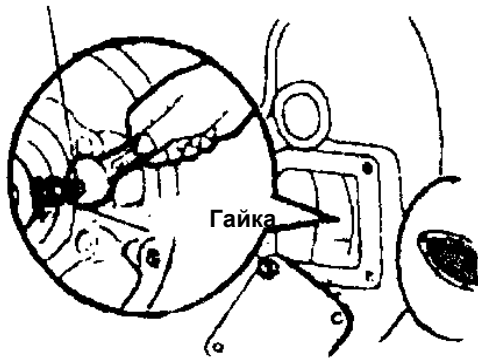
Регулировка зазора между отжимным кольцом и выжимным подшипником
